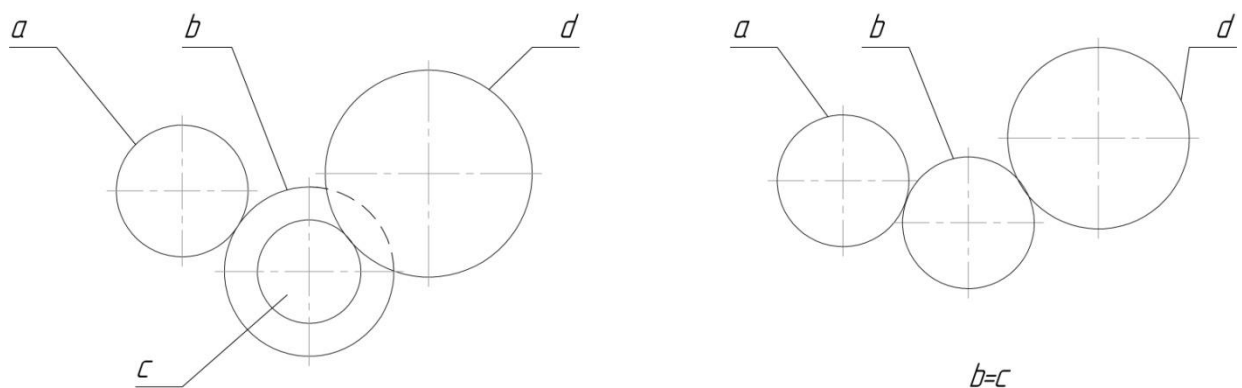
Схема гітари зубофрезерного верстата
